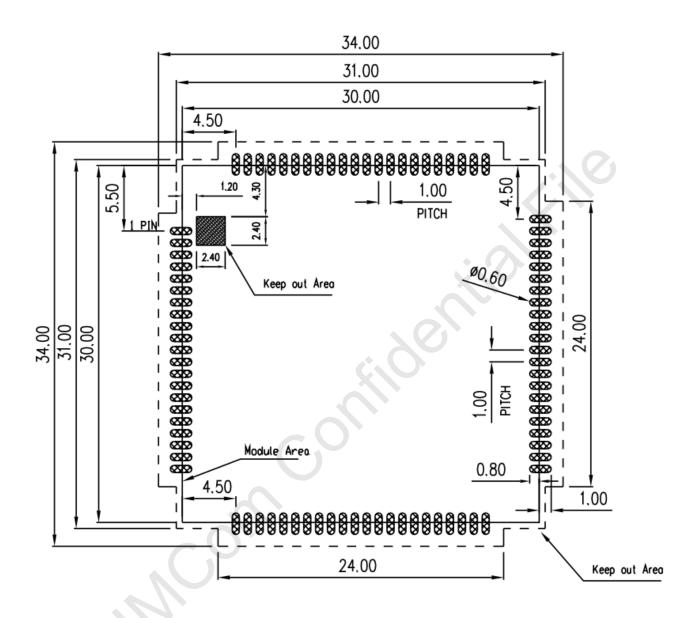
推荐 PCB 封装尺寸(单位:毫米)
